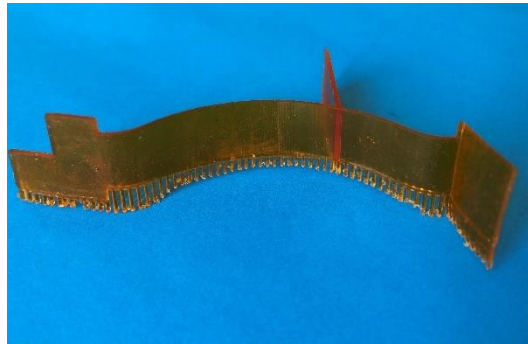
16. Döküm-Lingual Bar (5x1,5 mm)
